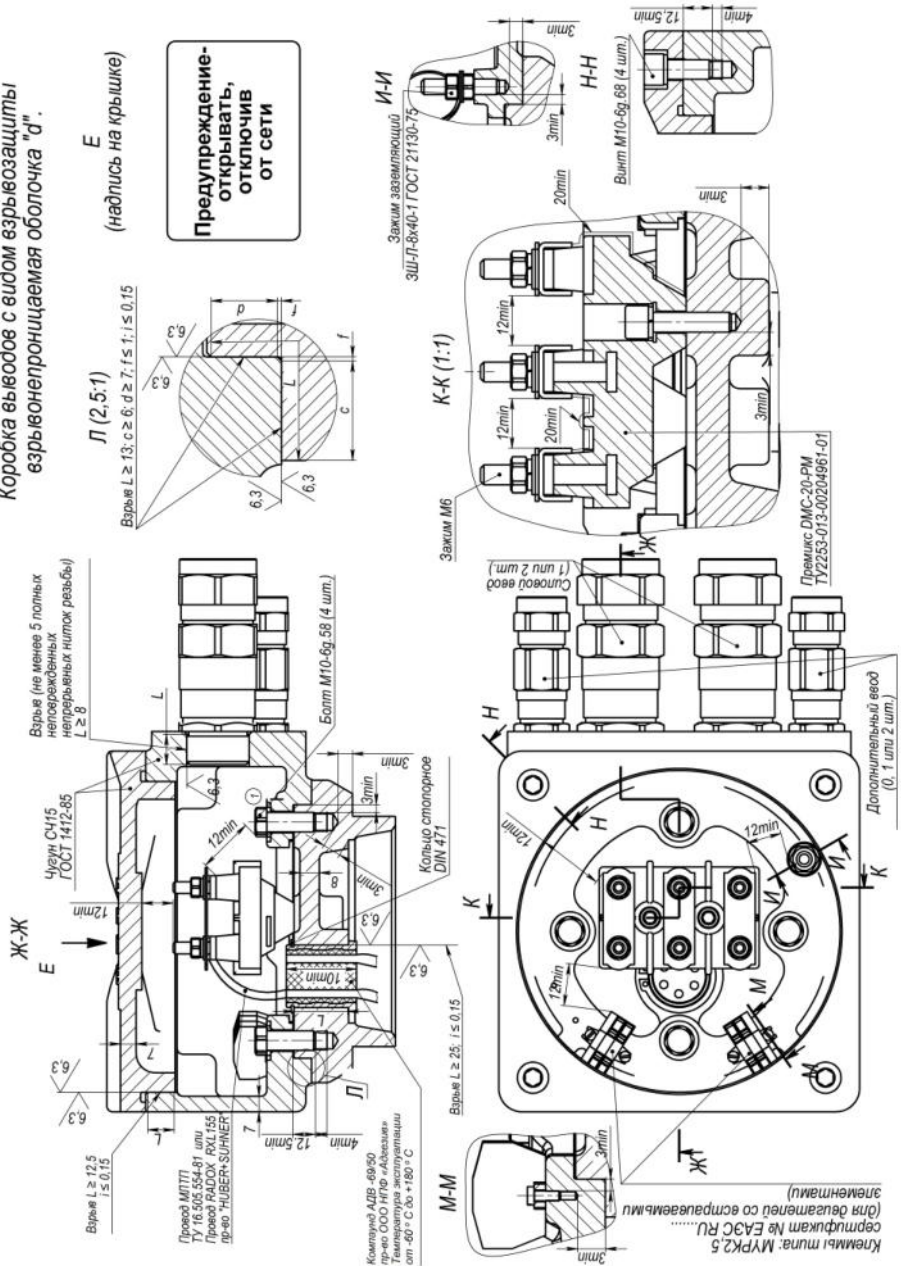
Чертеж взрывозащиты коробки выводов «d»
